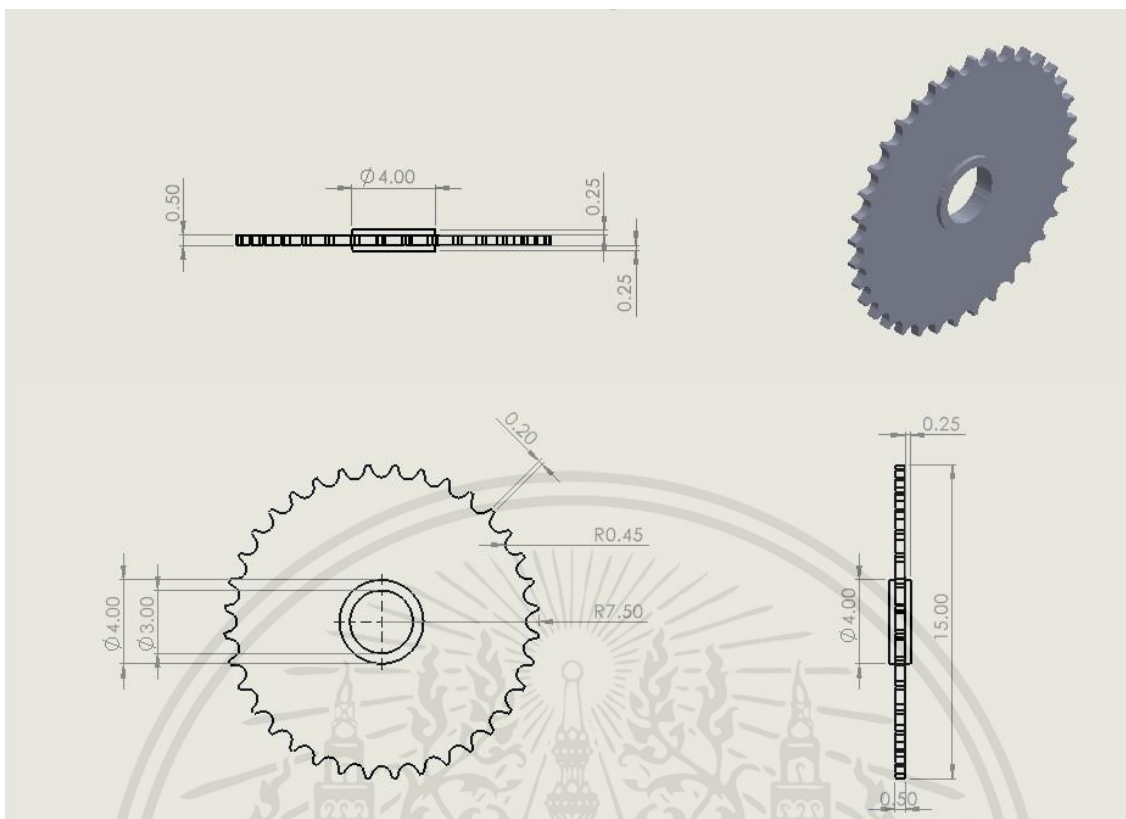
แบบโครงสร้างเครื่อง CAD
